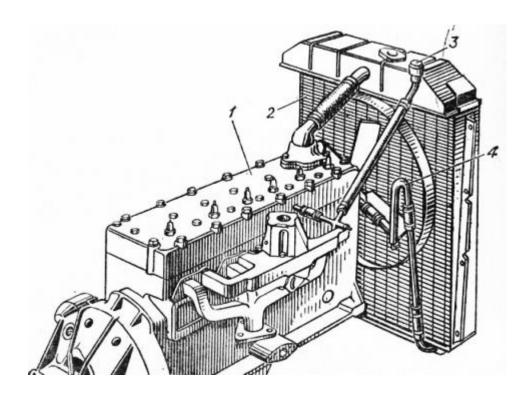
Схема оборудования двигателя для разогрева его горячей водой (способ НИИА): 1— двигатель; 2 —радиатор; 3 — заливная Еоронка; 4 — повышающая петля
